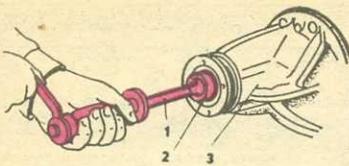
Проверка предварительного натяга в подшипниках ведущей шестерни динамометром: 1 — динамометр; 2 — переходная втулка или торцовая головка; 3 — картер редуктора.
